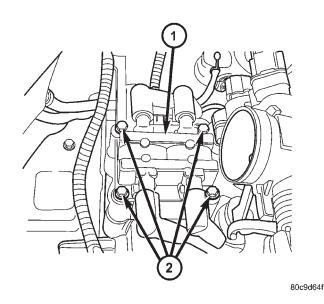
BOBINA DE ENCENDIDO - 2.4L
